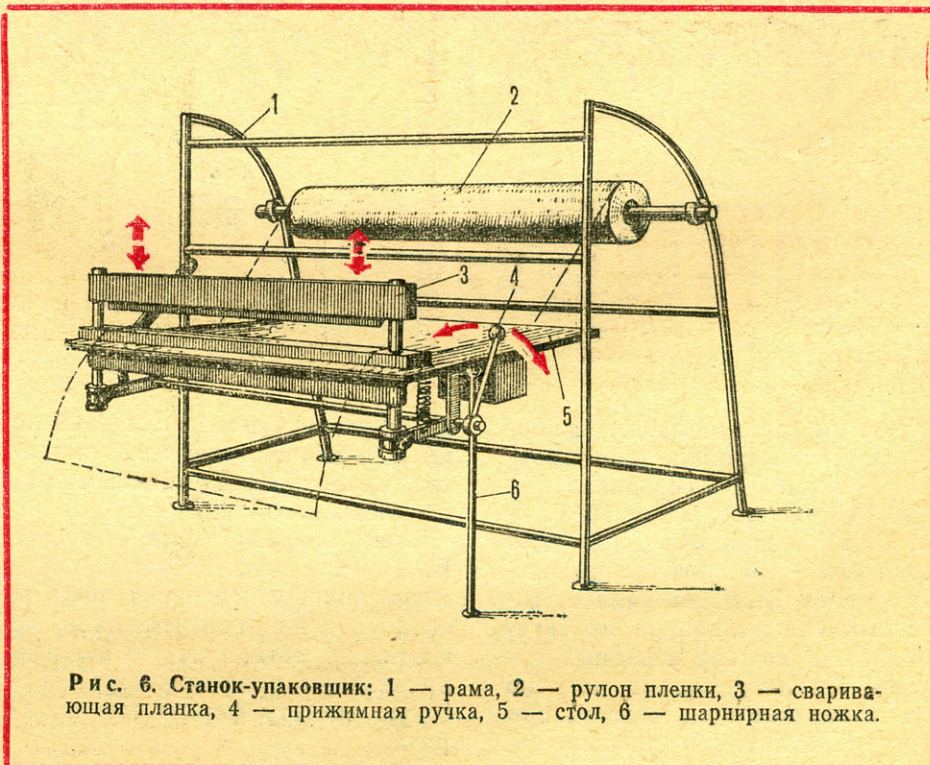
Станок-упаковщик: 1 — рама, 2 — рулон пленки, 3 — сваривающая планка, 4 — прижимная ручка, 5 — стол, 6 — шарнирная ножка.
